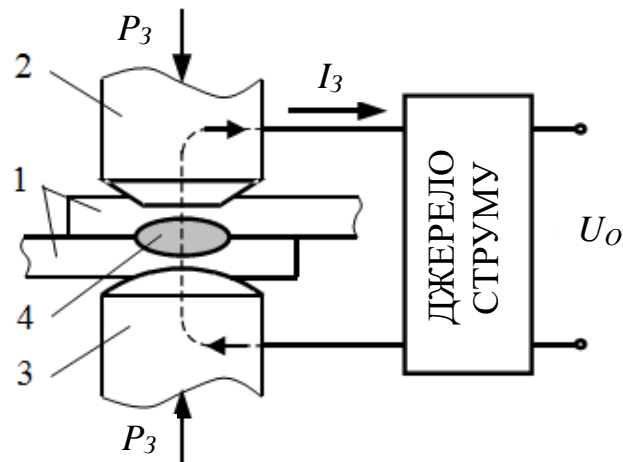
Схема двоконтактного точкового зварювання: 1 – деталь зварювання; 2, 3 – струмопровідні електроди; 4 – зварна точка
